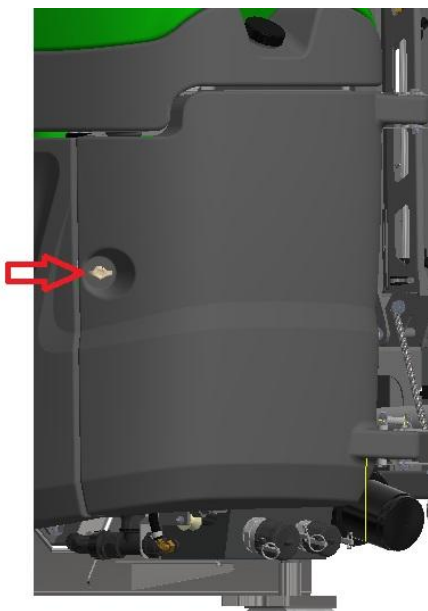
Puerta de acceso a la escalera, premezclador y válvulas de control
